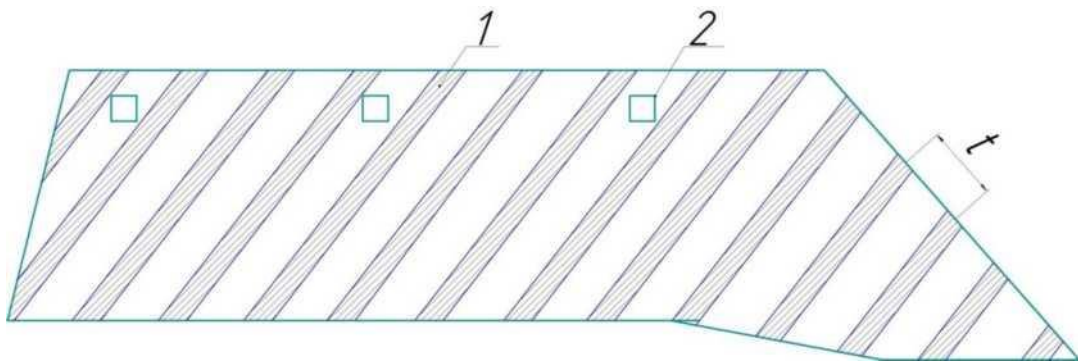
Схема наплавлення плужного леміша: 1 – наплавлений валик, 2 – отвори кріплення, t - крок наплавлення
